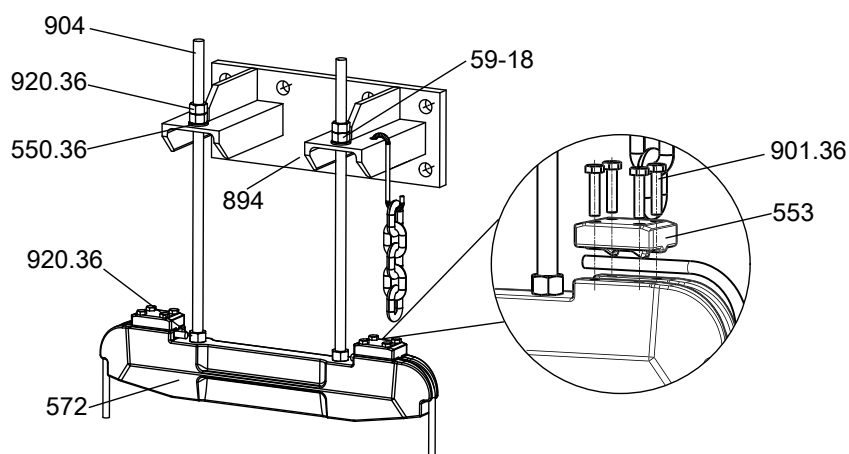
Исполнение консоли для типоразмеров с номинальным диаметром напорного патрубка DN 350, DN 400, DN 500, DN 600 и DN 700
